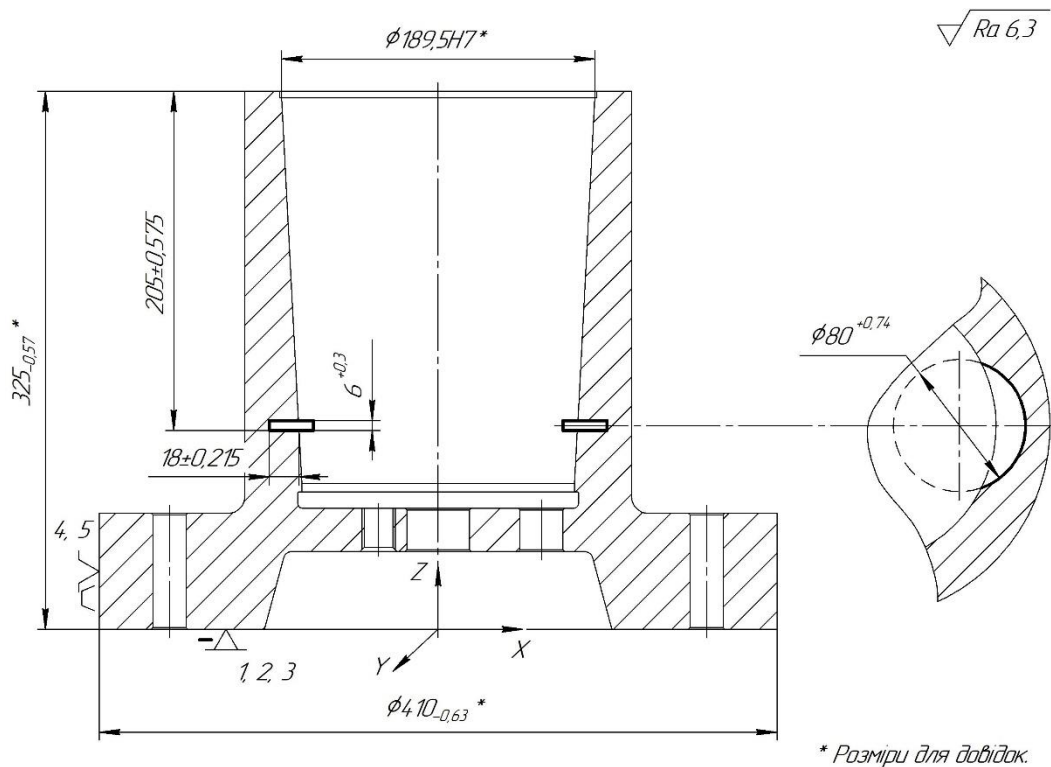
Альтернативна схема базування заготовки на операції фрезерній з ЧПК 110
